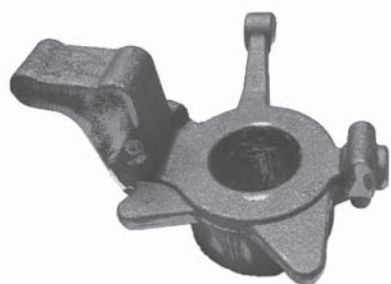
Отливка «Кулак поворотный» мод. ВАЗ-2116
